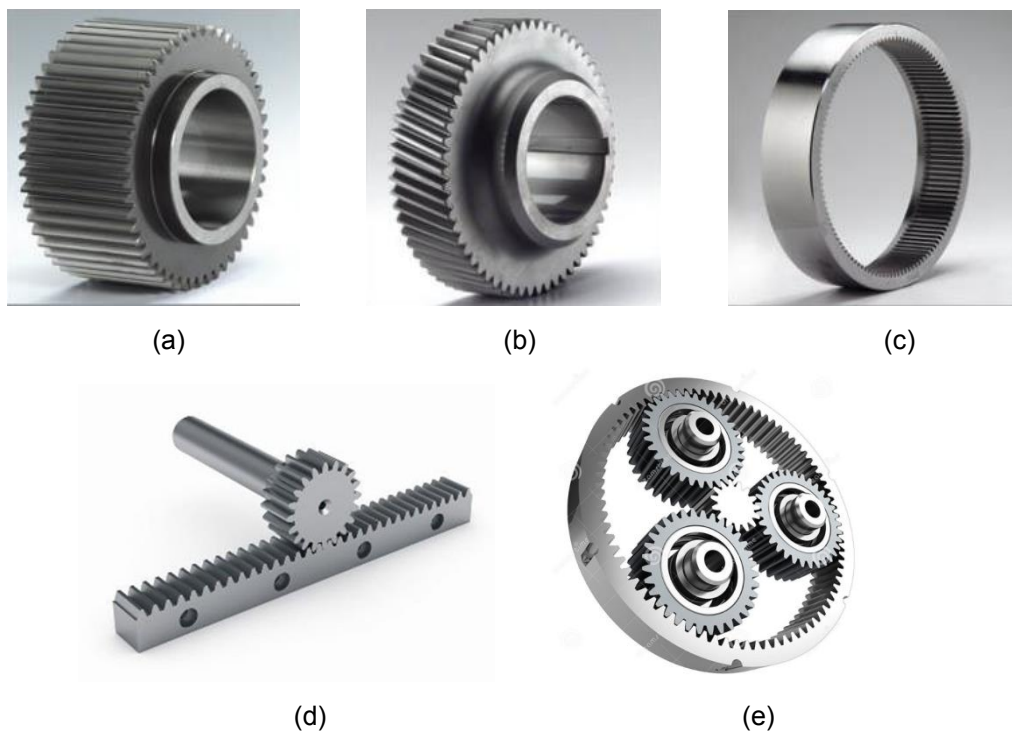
Engrenagens cilíndricas - (a) dentes retos; (b) dentes helicoidais; (c) engrenagem interna; (d) com cremalheira; (e) planetário
